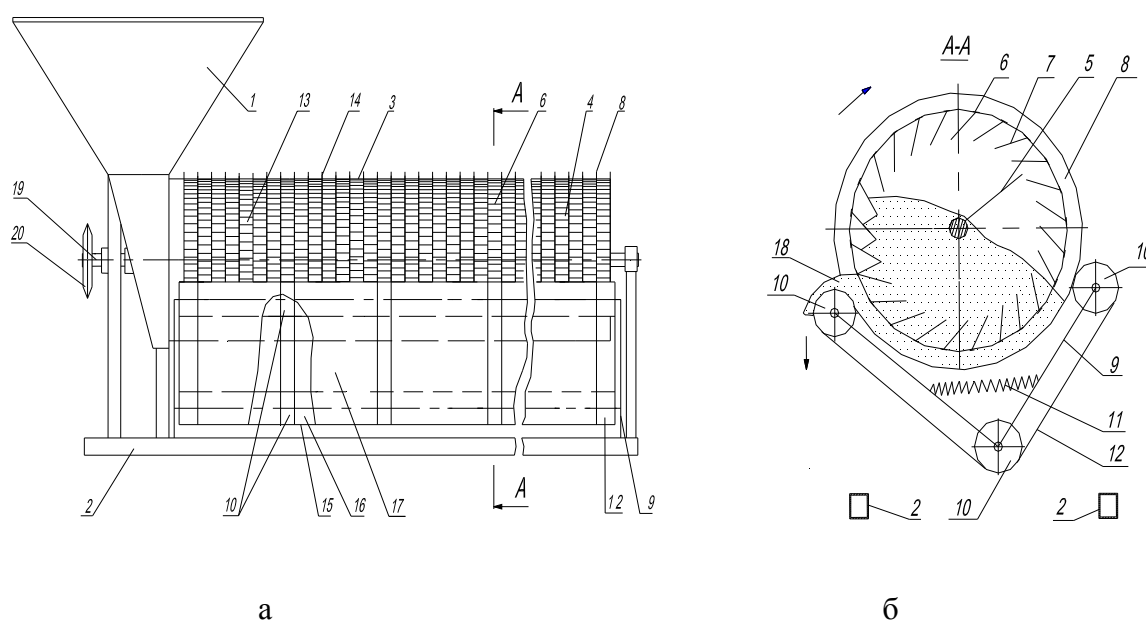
Удосконалений живильний устрій шнекової машини для поверхневого внесення сипучих мінеральних добрив: а – загальний вигляд; б – переріз живильного устрою.
